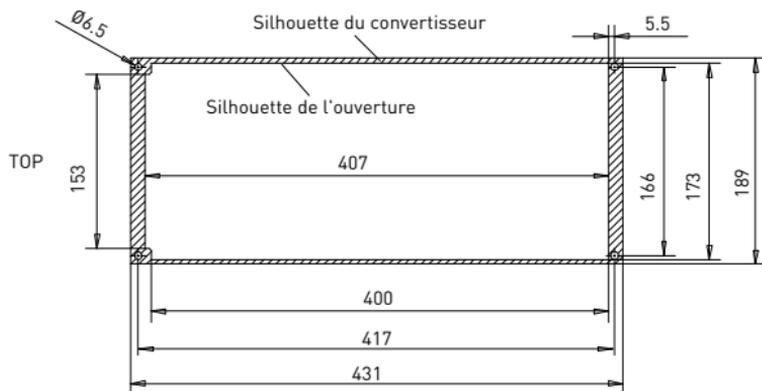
dimensions de découpe en montage par bride, pour MI5 (unité: mm)
